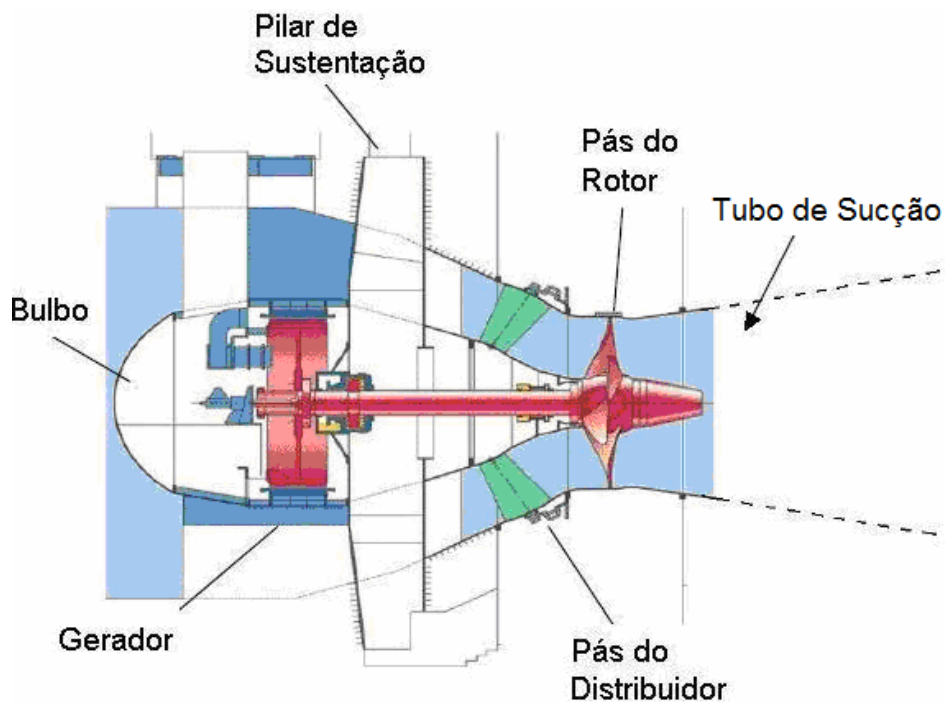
Visão em corte longitudinal - localização do tubo de descarga.
